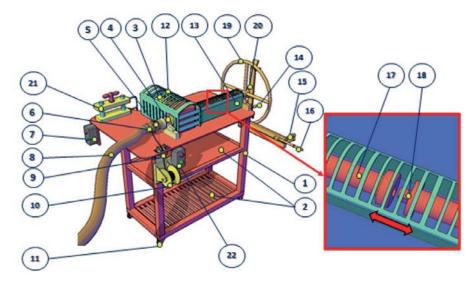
Комбинированный станок для обслуживания пожарных рукавов:
